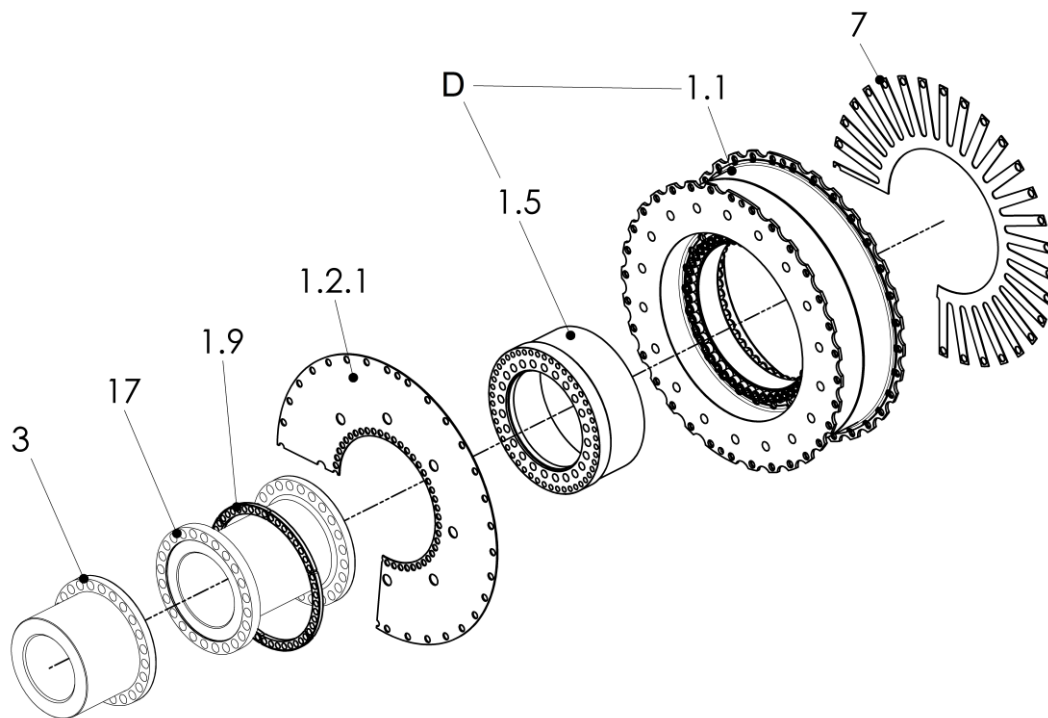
Beispiel: 020G-00050...00090-F.20
